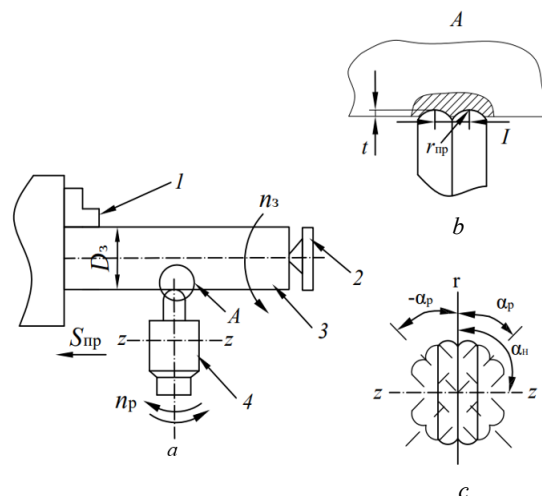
Схемы реверсивного ППД двухрадиусным роликом (а), его рабочей зоны (b) и реверсивного вращения (с): 1 – трехкулачковый патрон; 2 – задняя бабка; 3 – заготовка; 4 – рабочий инструмент
